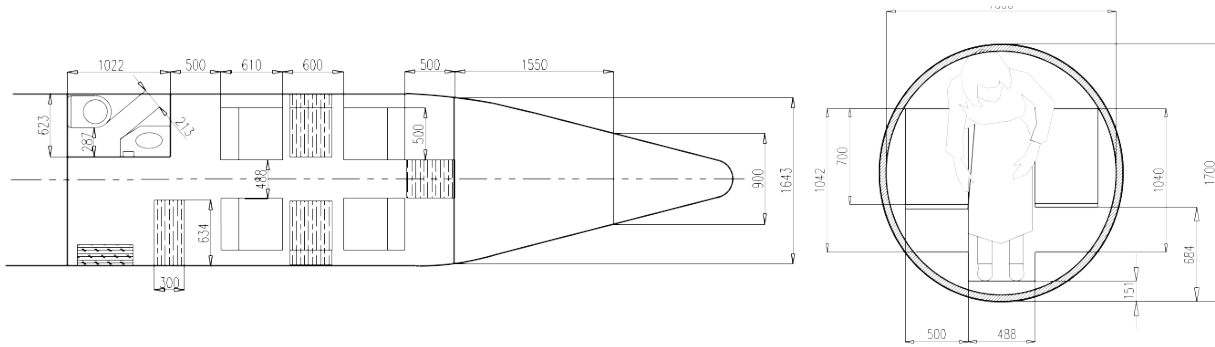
Vista en planta y de una sección de la cabina de pasaje
